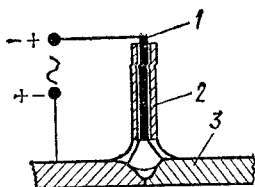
Ручная сварка плавящимся электродом, покрытым обмазкой
